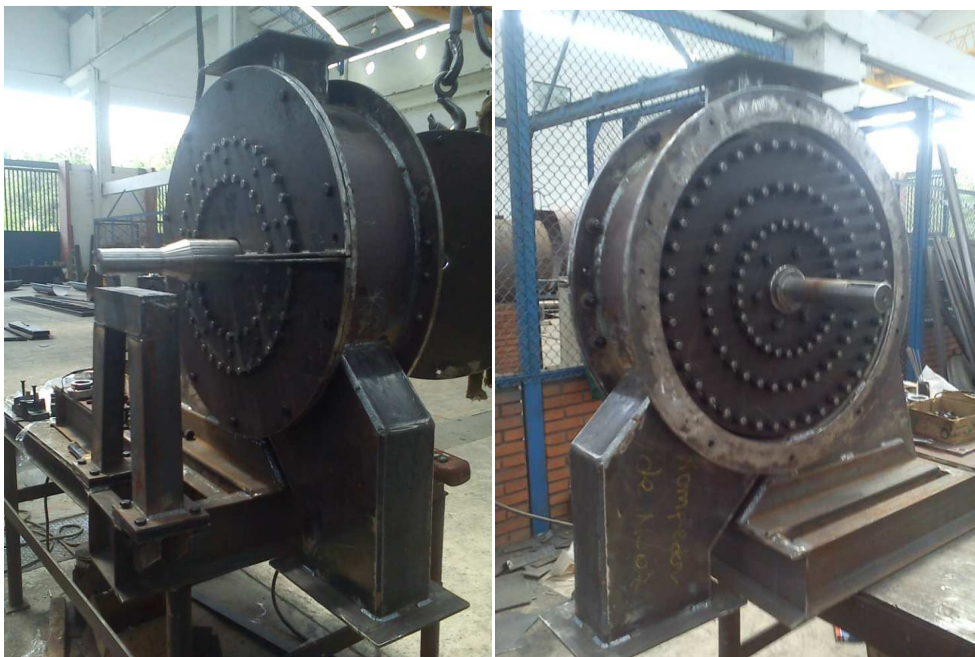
Ensamble tapa posterior y barras fijas sobre ensamble soldado carcasa
